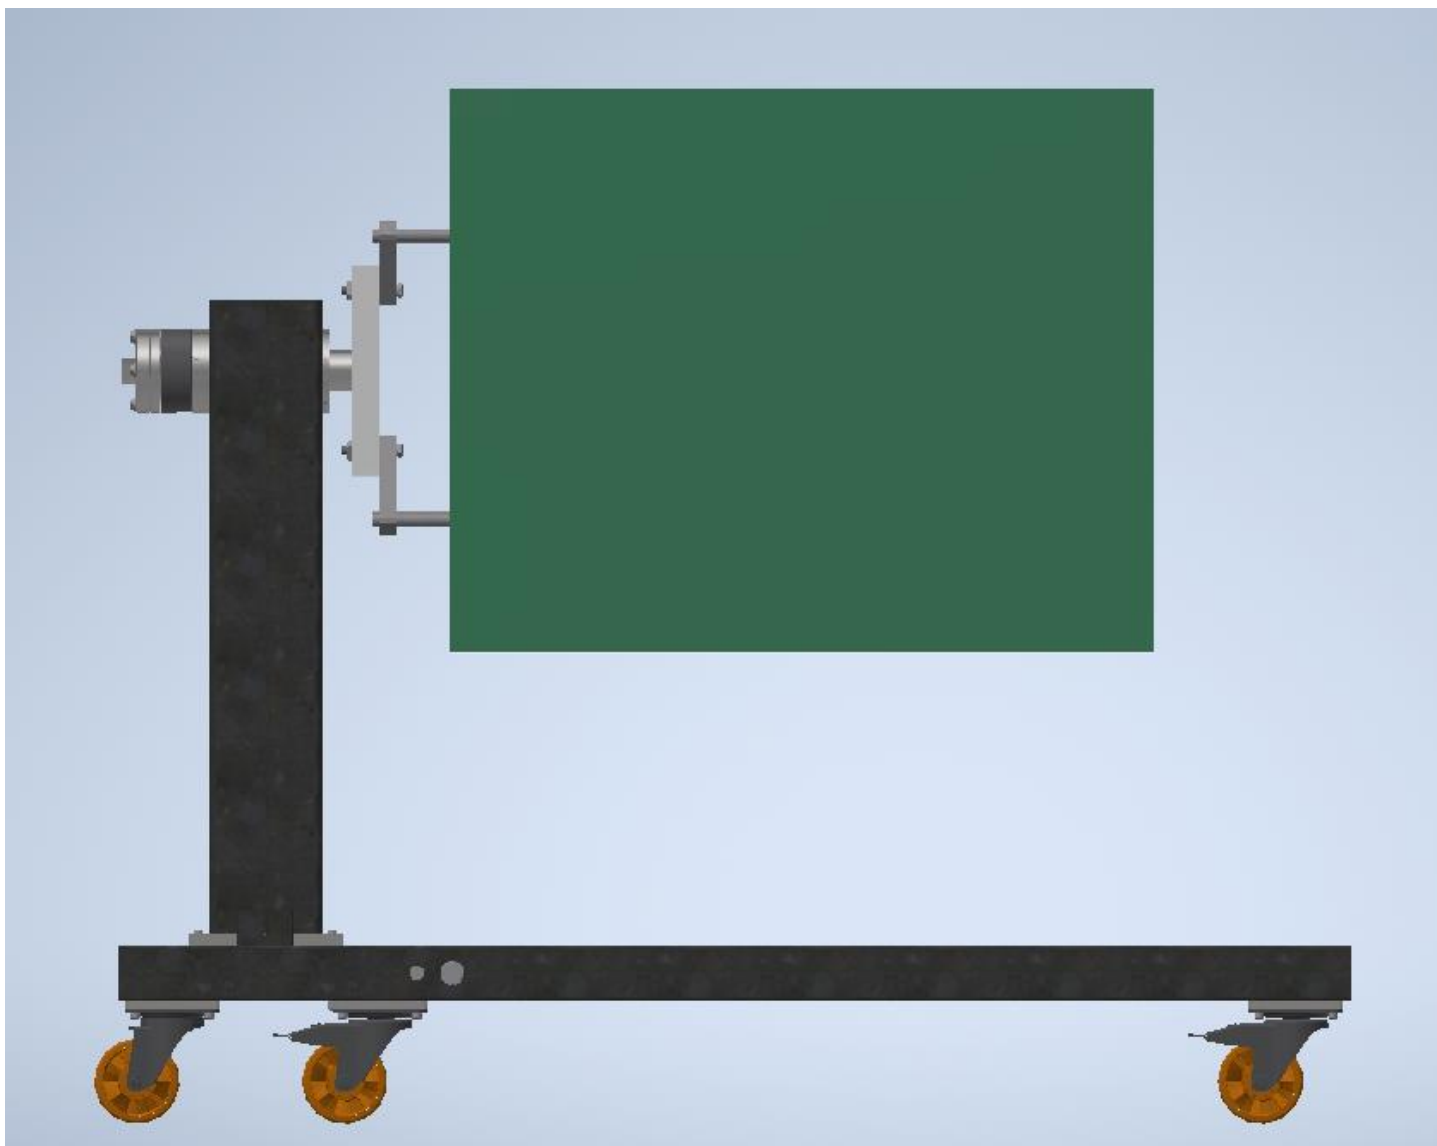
Motor-Montagevorrichtung Seitenansicht mit Motor
